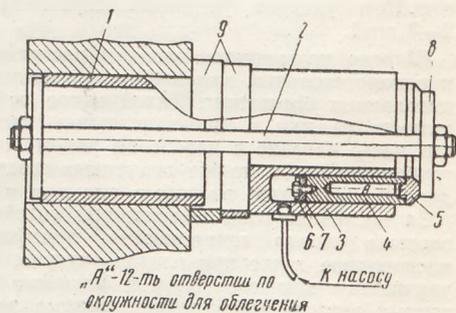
Выпрессовка втулки гидравлическим домкратом новой конструкции:
